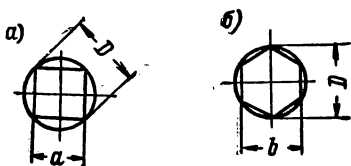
Эскизы для расчета диаметров заготовок под квадрат и шестигранник.
